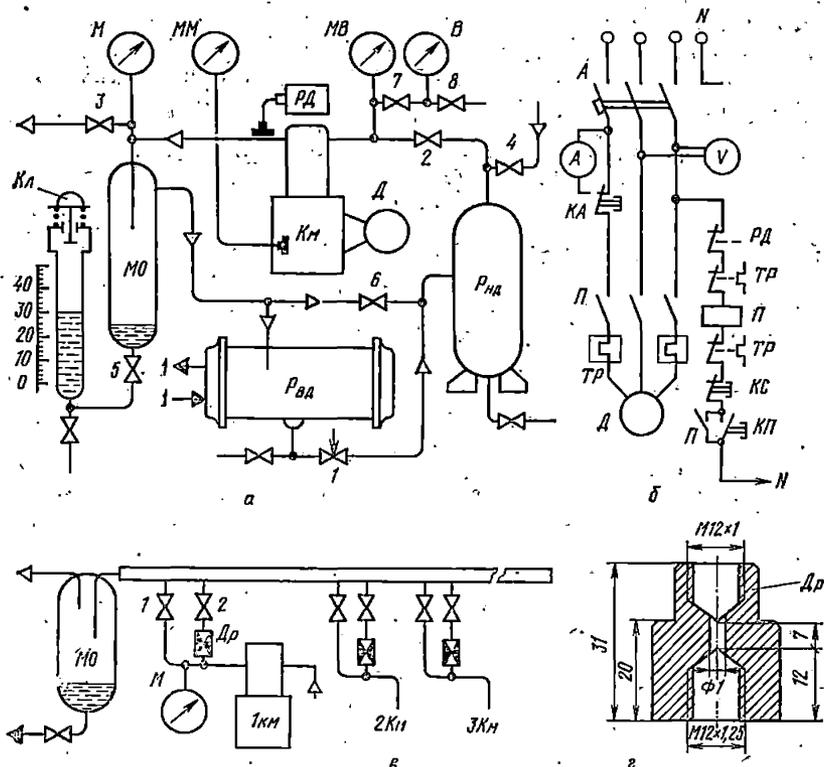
Стенд обкатки компрессоров: а — для средних и крупных компрессоров; б — электросхема; в — для малых компрессоров; г — дрессель
